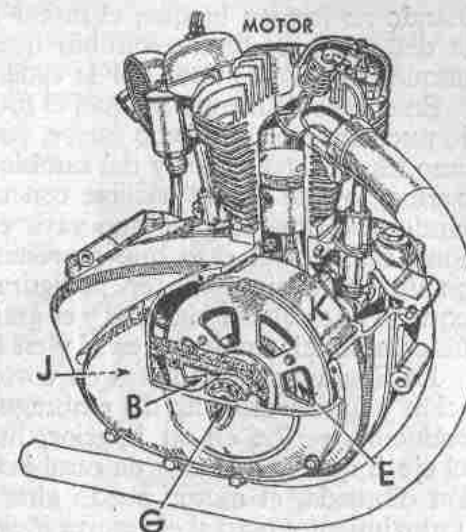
A.—Bloque motor con el embrague al extremo del cigüeñal y enlace por cadena con el cambio.
